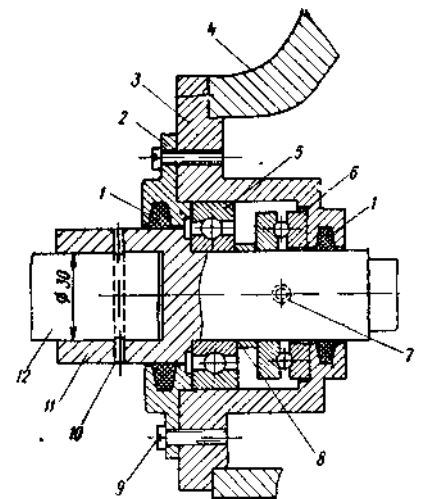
Упорно-опорный подшипник для двигателя М-21.
